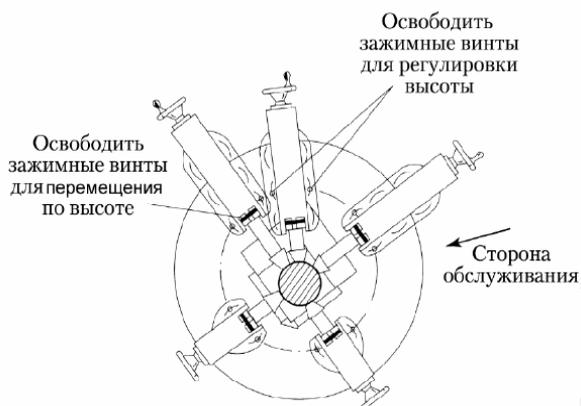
Схема крепления штампа в кулачках штамподержателя
